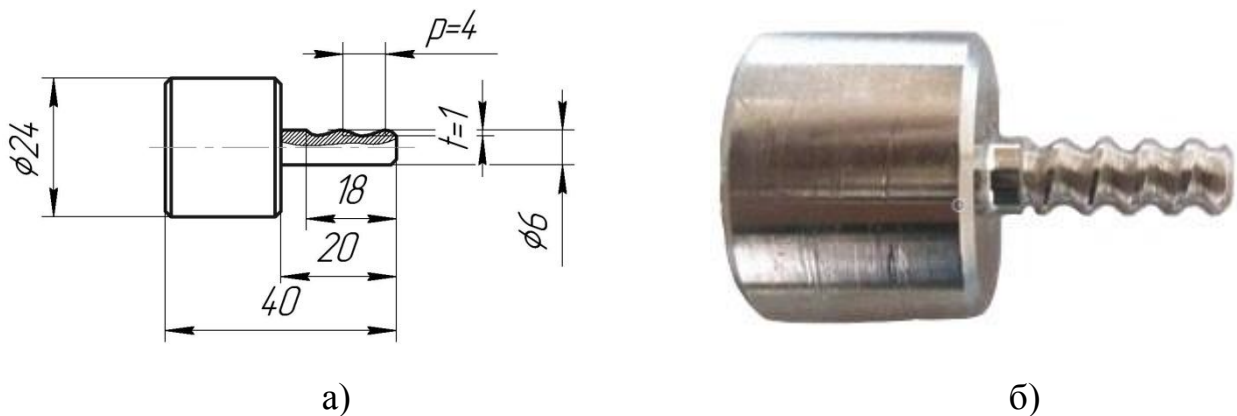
Металева вставка круглої зовнішньої різьби: а) ескіз металевої вставки; б) фото вставки [99]
